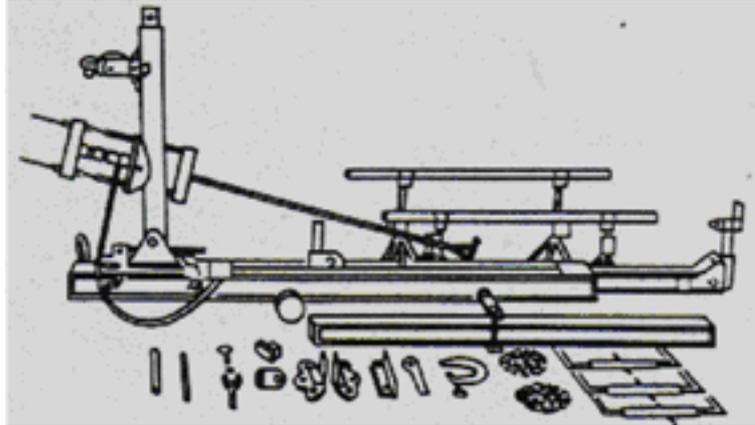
Escuadra de enderezar carrocería portátil.
